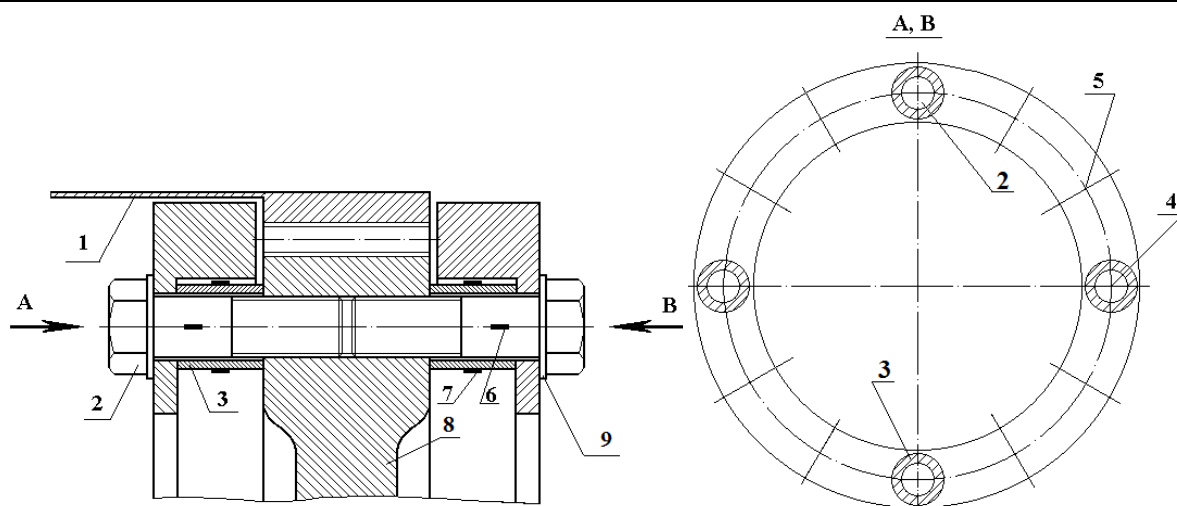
Сопряжение гибкого колеса со ступицей выходного вала редуктора:
